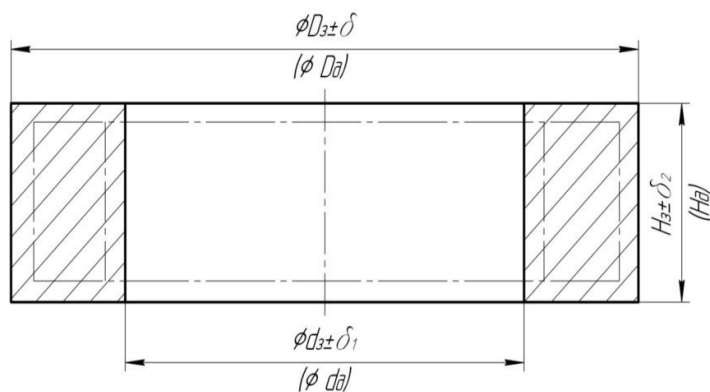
Креслення кованої деталі «Кільце»
